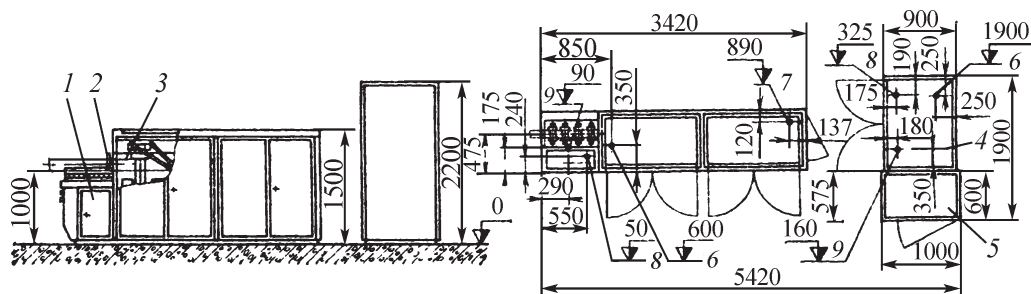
Рекомендуемая планировка размещения кузнечного нагревателя:
